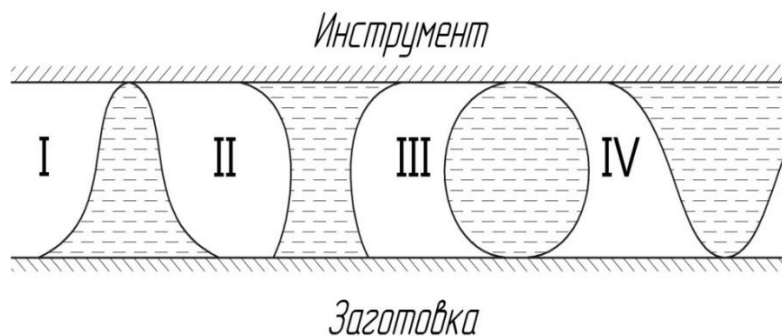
Формы капель смазки, наносимой на инструмент или заготовку
